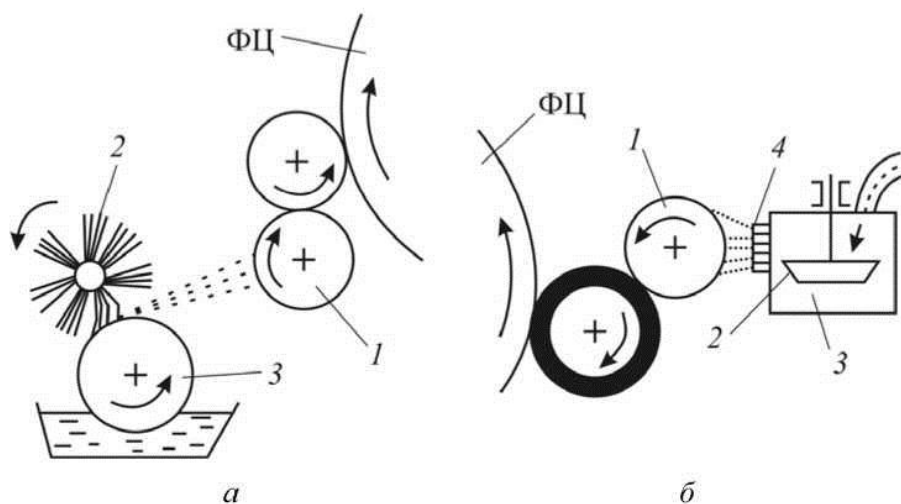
Контактные увлажняющие аппараты с бесконтактным питанием: а - щеточного типа; 1 - раскатной цилиндр; 2 - щетка; 3 - дуктор; б - роторного типа; 1 - раскатной цилиндр; 2 - ротор; 3 - кожух; 4 - сетка; ФЦ - формный цилиндр
